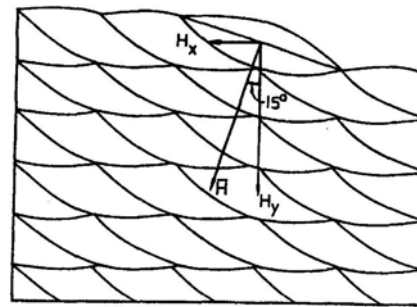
Direction du flux thermique pour une soudure à plat [16].
